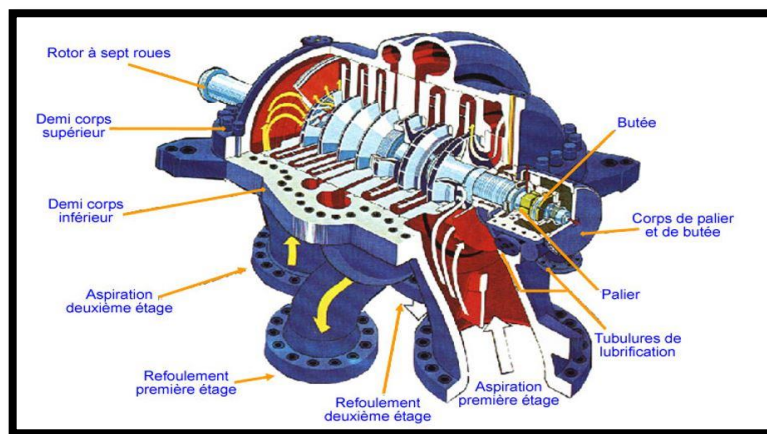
Compresseur centrifuge avec plan de joint horizontal et à deux étages [11]
